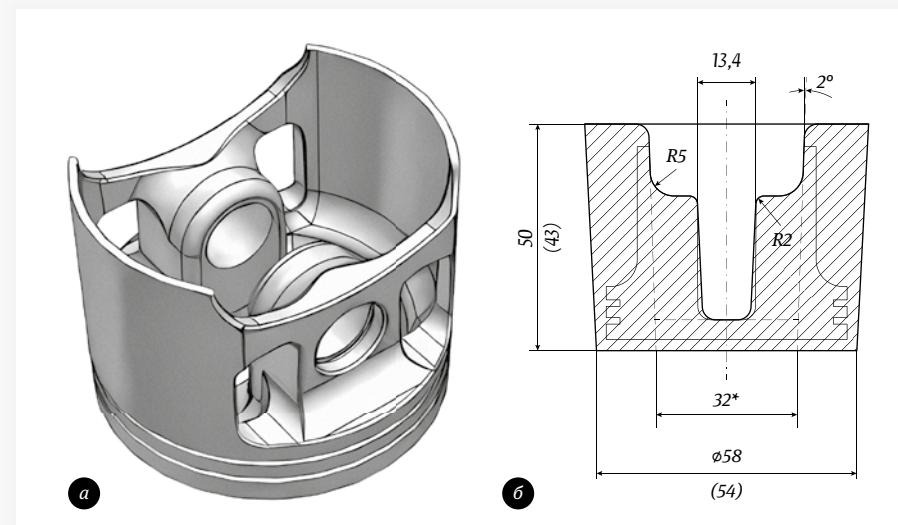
Штамповка поршня из алюминиевого сплава АК4-1: *а* – деталь «поршень», *б* – штамповка детали «поршень» [14]
